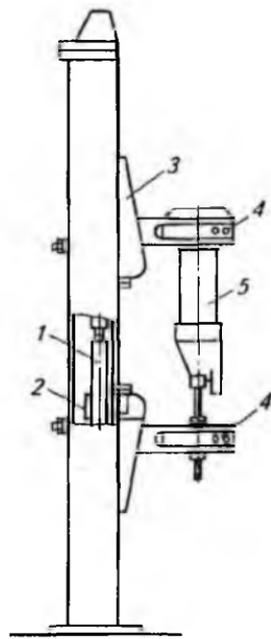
Схема приспособления для разборки доильных стаканов аппарата АДУ-1:
